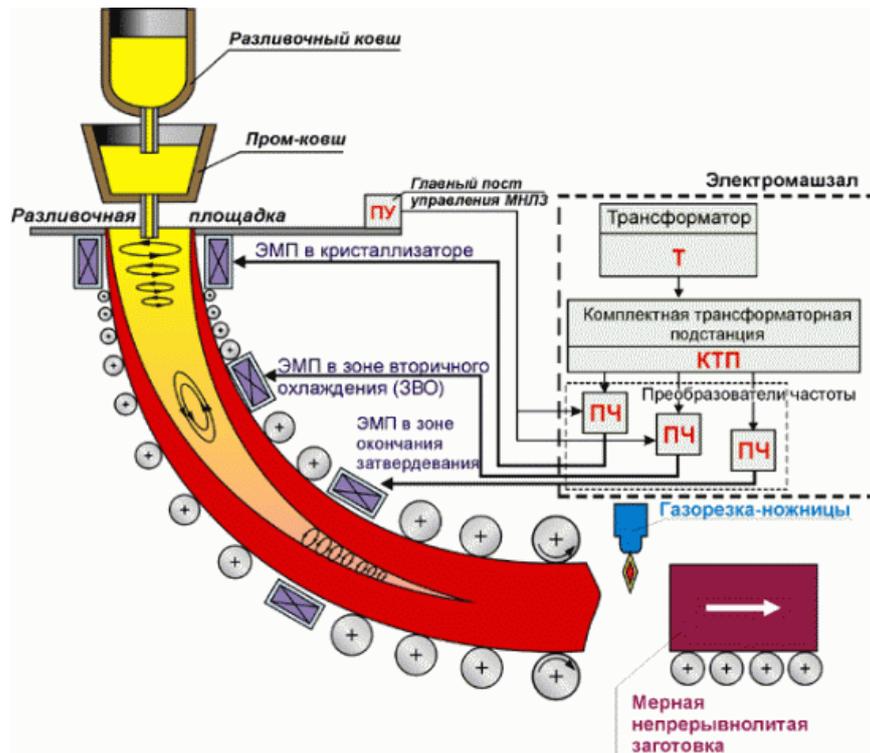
Схема разливки стали на МНЛЗ
